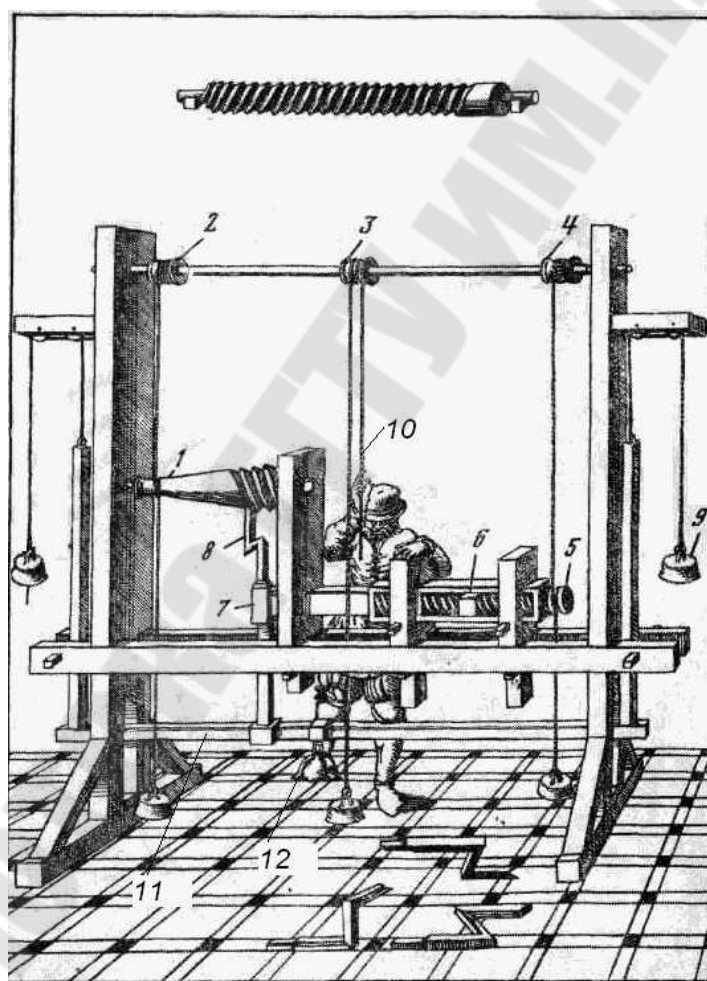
Рисунок токарно-винторезного станка (по Жаку Бессону 1569г.):
